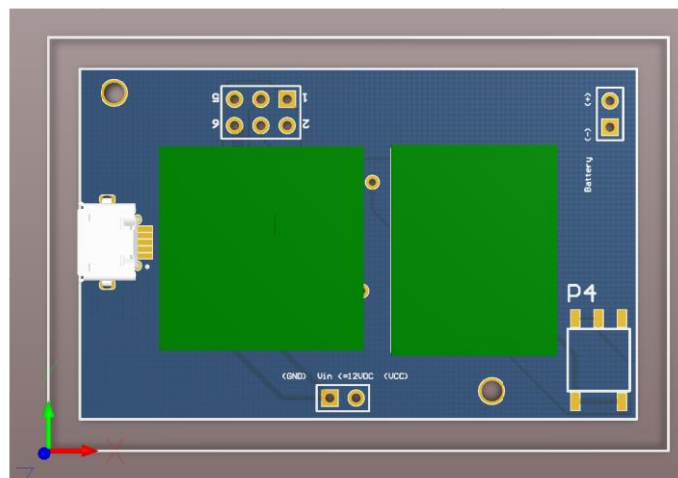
Resultado del PCB Final visto desde la Capa Superior [20]
